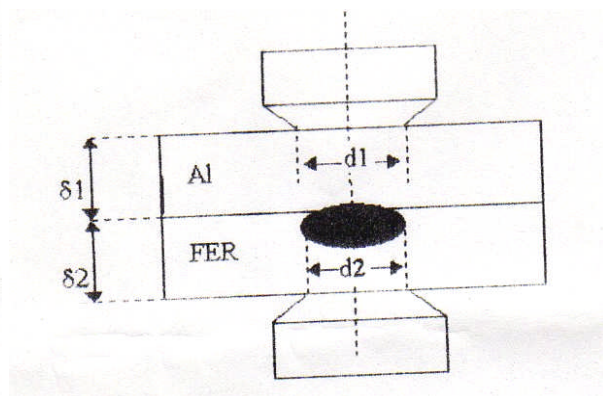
soudage de deux pièces avec électrodes différents diamètre
